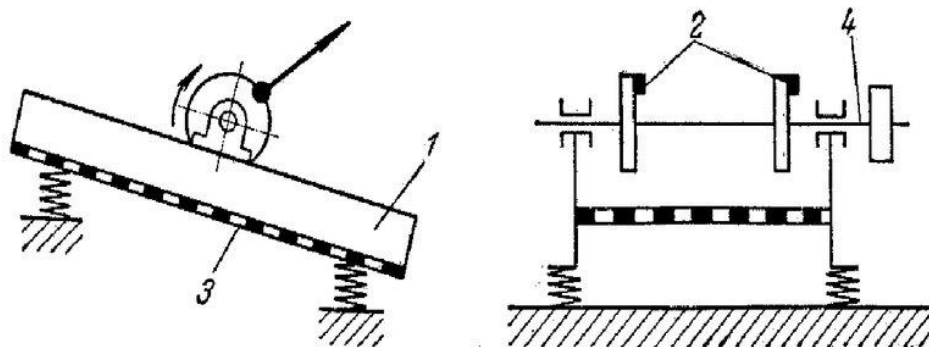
Схема привода решета с дебалансами: 1 - решетный стан; 2 - дебалансы; 3 - решето; 4 - вал
